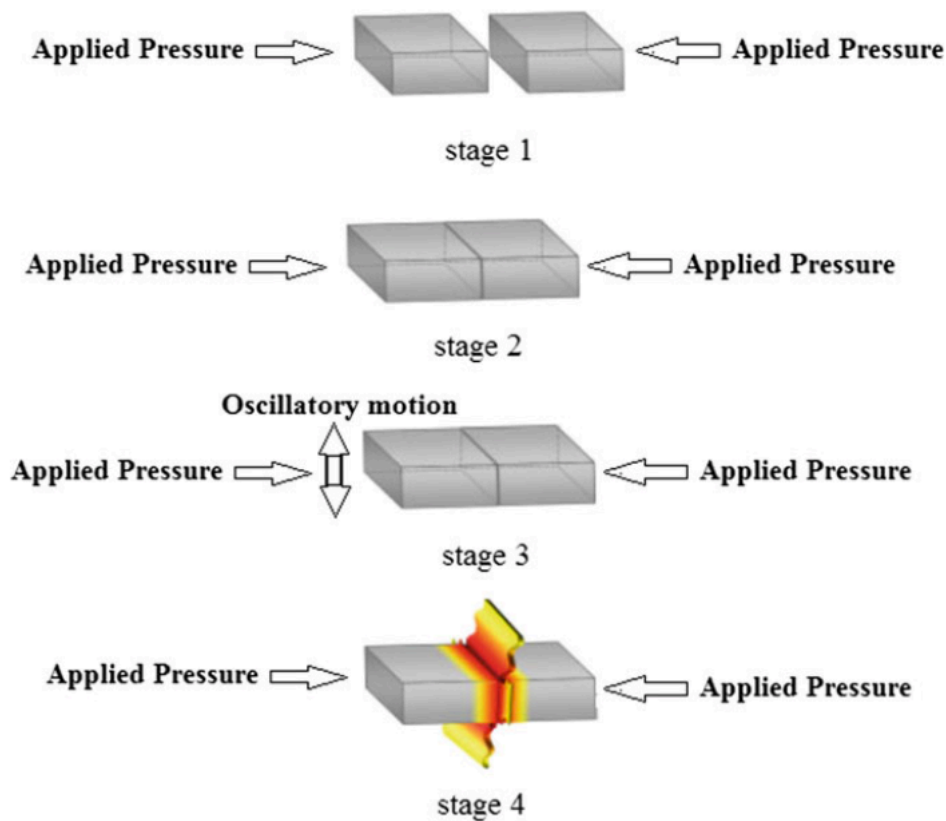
Etapas del proceso de soldadura por fricción. [2]
